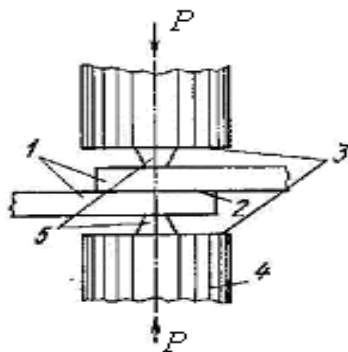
Схема холодной сварки: 1 – свариваемые заготовки, 2 – зачищенные поверхности свариваемых заготовок, 3 – поверхности пуансонов, 4 – пуансоны, 5 – выступы пуансонов
